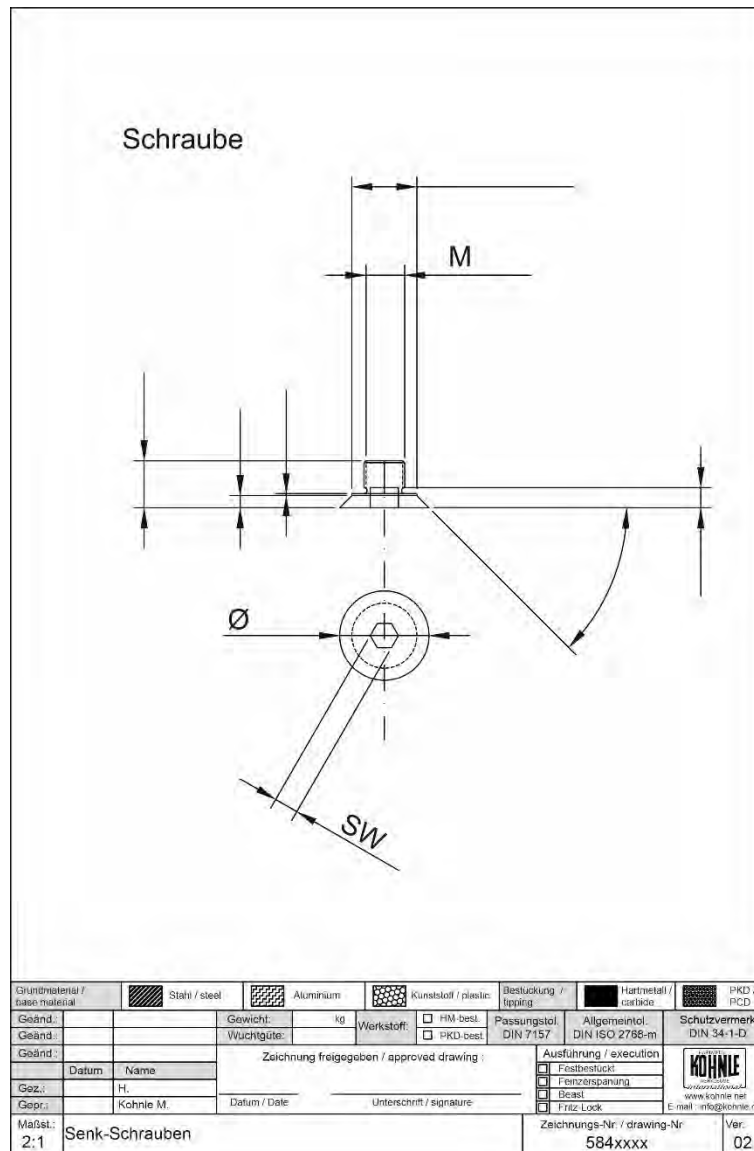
Zeichnung der Schraube aus der Mastodon-Schraubverbindung
